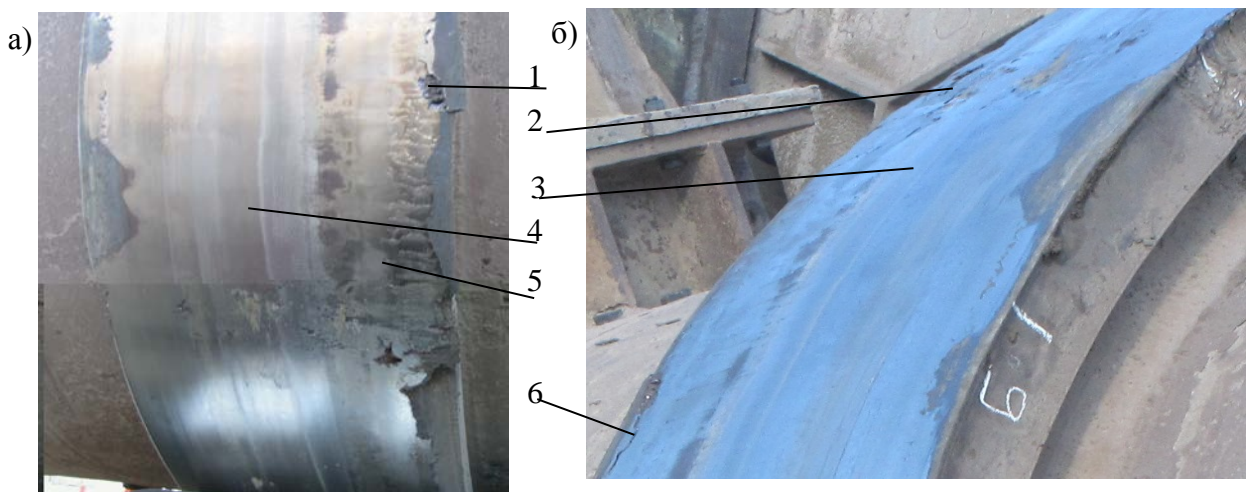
Повреждения поверхностей катания бандажей типа В вращающейся печи 5×185 м: 1- отслаивание материала на торцевой поверхности бандажа; 2 - неровности в месте сварки; 3,4 - следы неравномерного износа; 5 - завальцовка кромок ("грибы"); 6 - трещина кромочного излома
